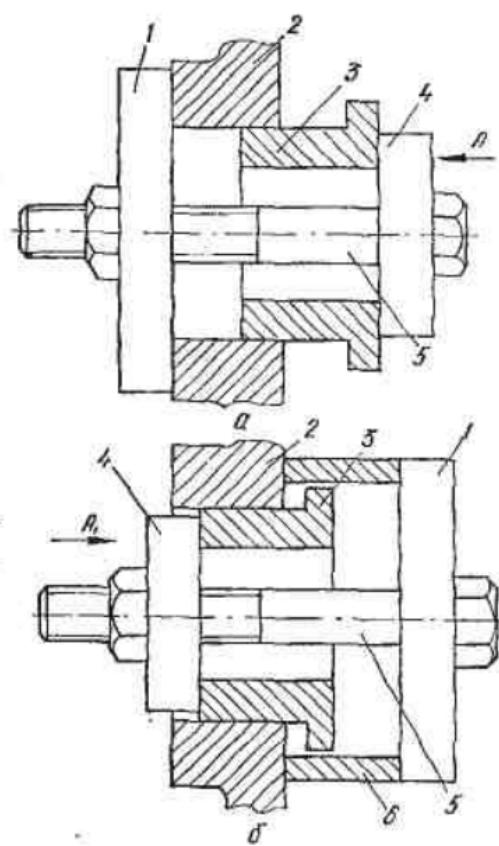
Схема запрессовки (а) и выпрессовки (б) втулки корпуса редуктора:
